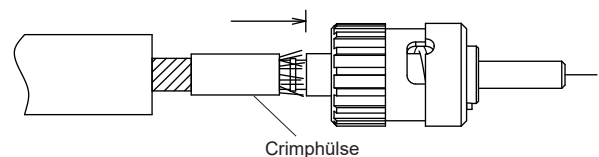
F-ST Steckverbinder mit Crimphülse und Knickschutztülle
